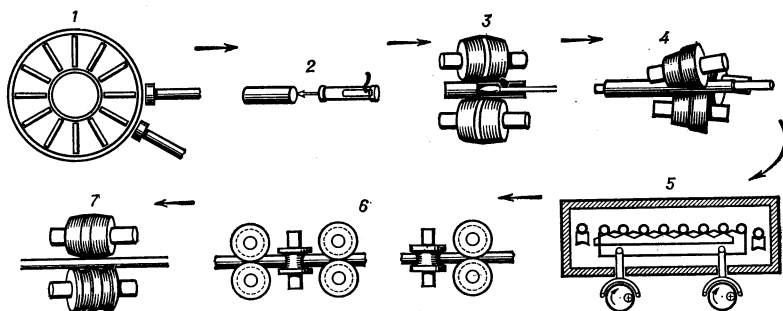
Схема технологического процесса производства труб на трубопрокатном агрегате с трёхвалковым удлинительным станом: 1 — нагрев исходной заготовки; 2 — центровка заготовки; 3 — прошивка заготовки на прошивном стане; 4 — раскатка на трёхвалковом стане; 5 — промежуточный подогрев заготовки; 6 — прокатка на редуционном стане; 7 — калибровка трубы на стане поперечно-винтовой прокатки.
